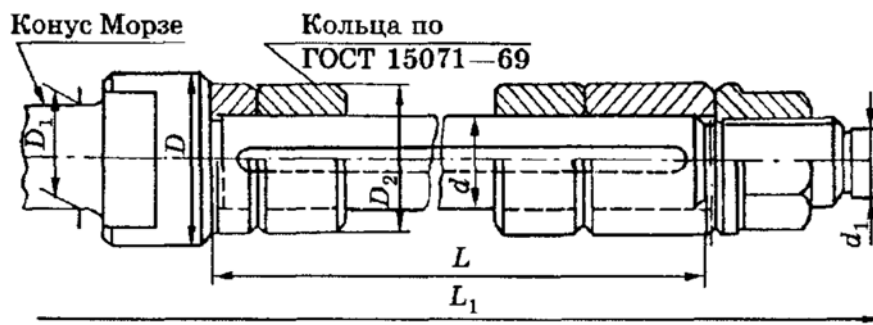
Оправка для крепления дисковых и цилиндрических фрез с передачей крутящего момента при помощи продольной шпонки
